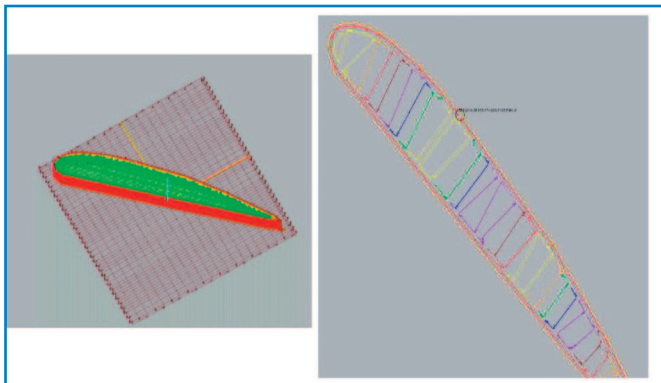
Diagramas 2D y 3D que muestran el plan de construcción de un ala modular.
